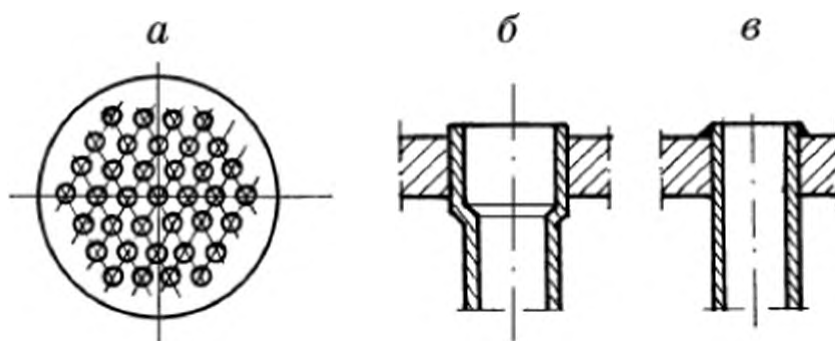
Способы размещения (а) и способы герметичного крепления концов труб в трубной решетке развальцовкой (б) и сваркой (в)
